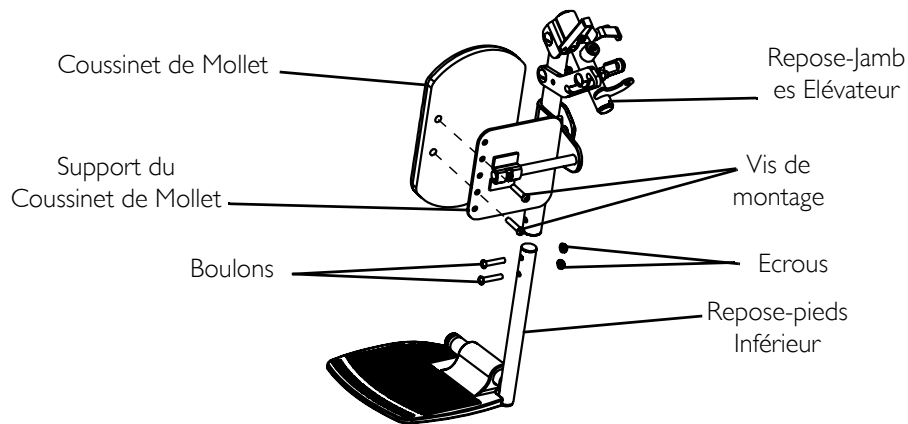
Régler la Hauteur du Repose-pieds - Réglage du coussinet de mollet
